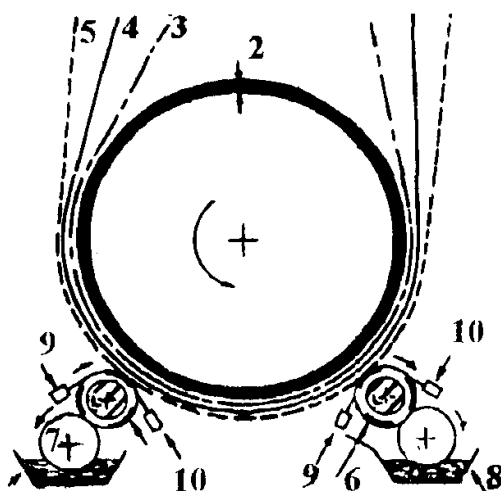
Технологическая схема печатной машины с цилиндрическими гравированными валами с двумя установленными печатными местами:
